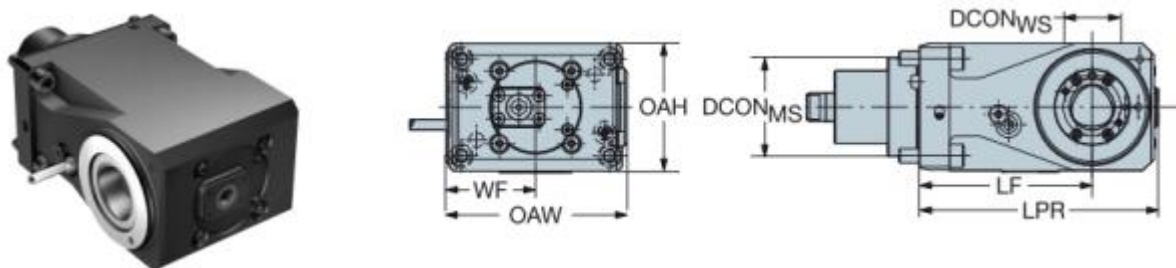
Инструментальные блоки ВМТ-Р для приводного инструмента
